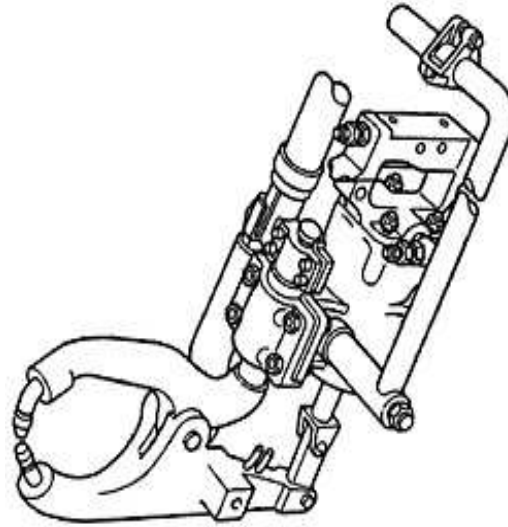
Esquema de uma máquina de solda típica: Tipo X - Cable Gun.
